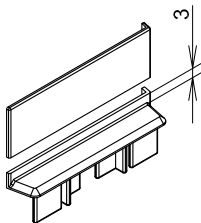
Bearbeitung der Endkappe 9C24 unten. Zuschnitt wie oben (Abb.2) und zusätzliches Entfernen des Überstandes.
